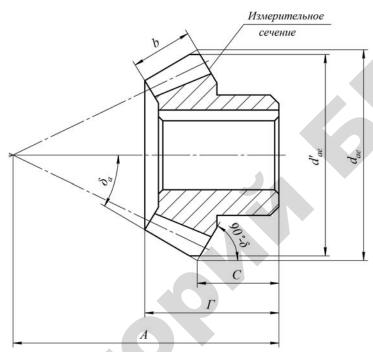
Простановка основных размеров для зубчатого конического колеса
